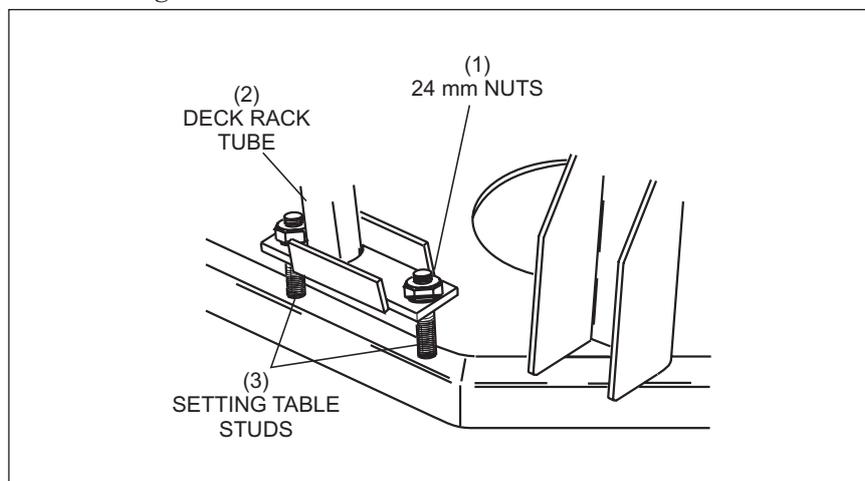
Enlever le plateau des tubes de support du quillier.
